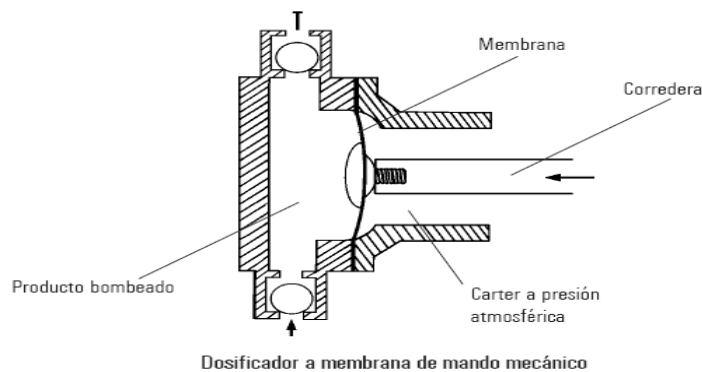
Conjunto Mecánico de la Bomba Dosificadora
